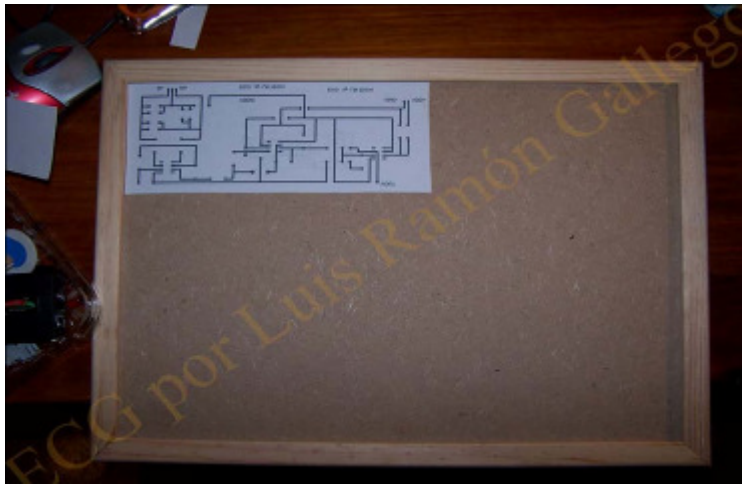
La plantilla está impresa con la opción “Mirror” para que todo encaje al darle la vuelta.
